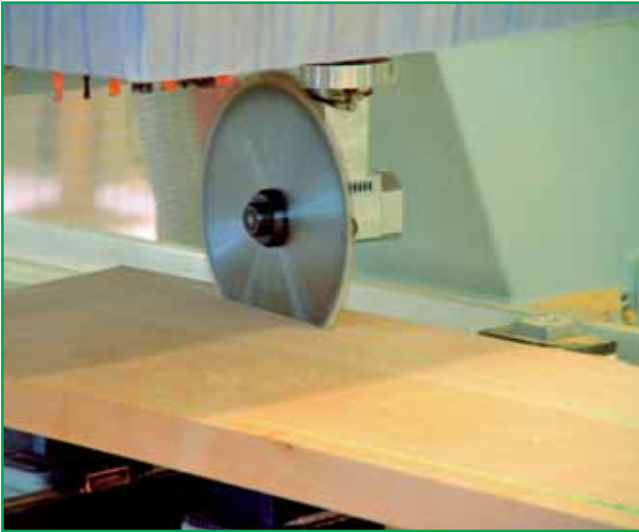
/1: Sägeaggregat, 4-achsige Bearbeitung
